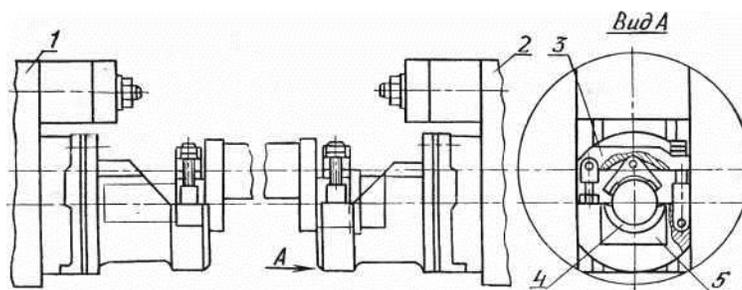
Установка коленчатого вала в кругло-шлифовальный станок
